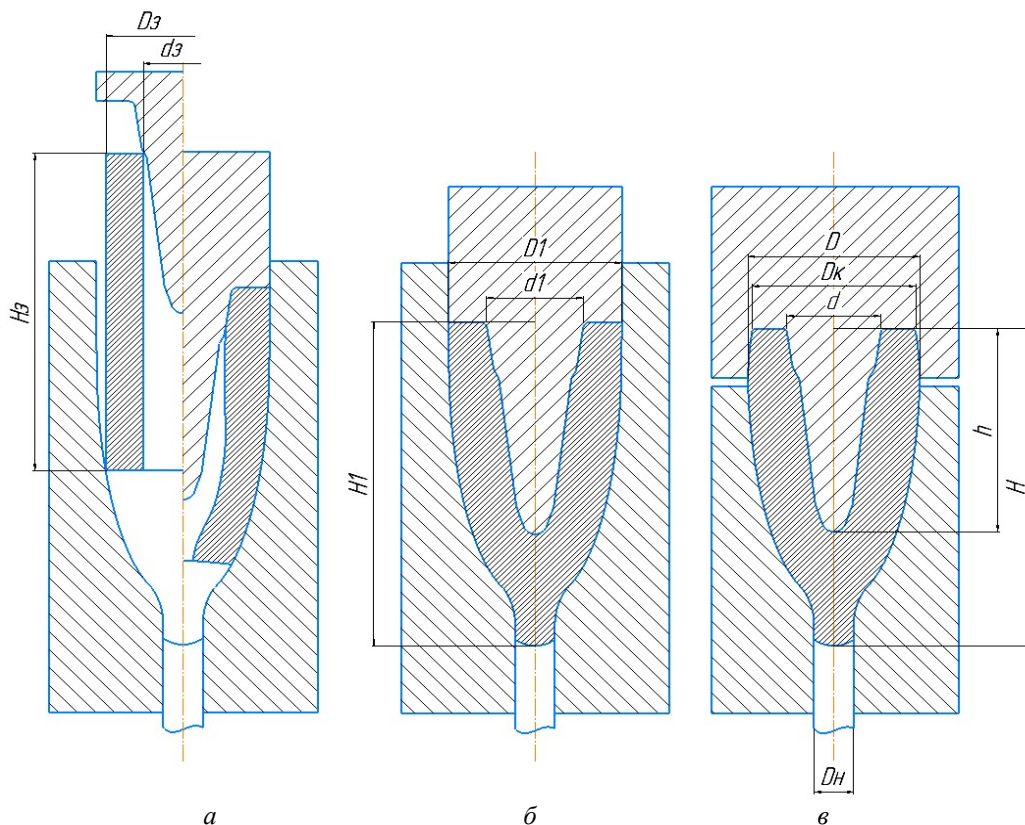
Технологические переходы горячей штамповки поковки типа оправки прошивного стана из трубной заготовки: а-установка заготовки в штамп; б, в - первый и второй переходы штамповки
